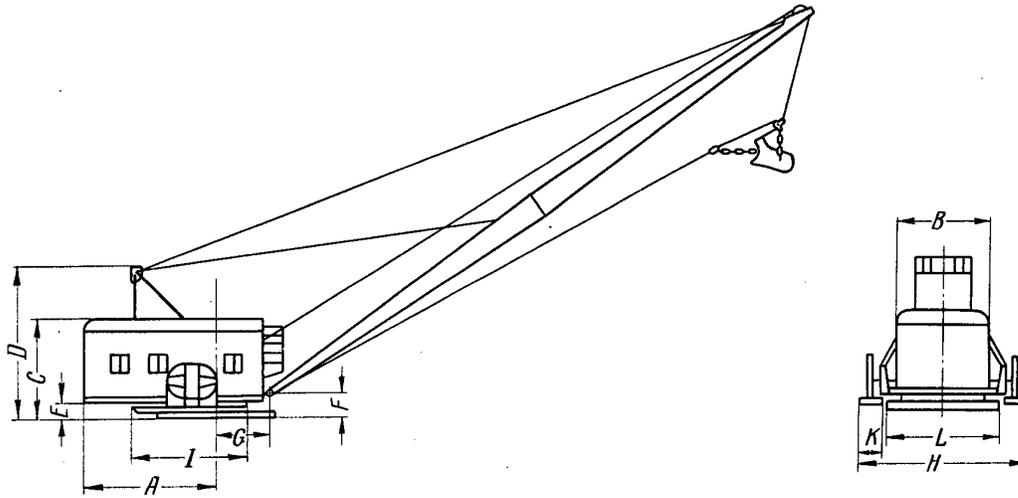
Габаритные размеры шагающего экскаватора модели ЭШ-4/40
